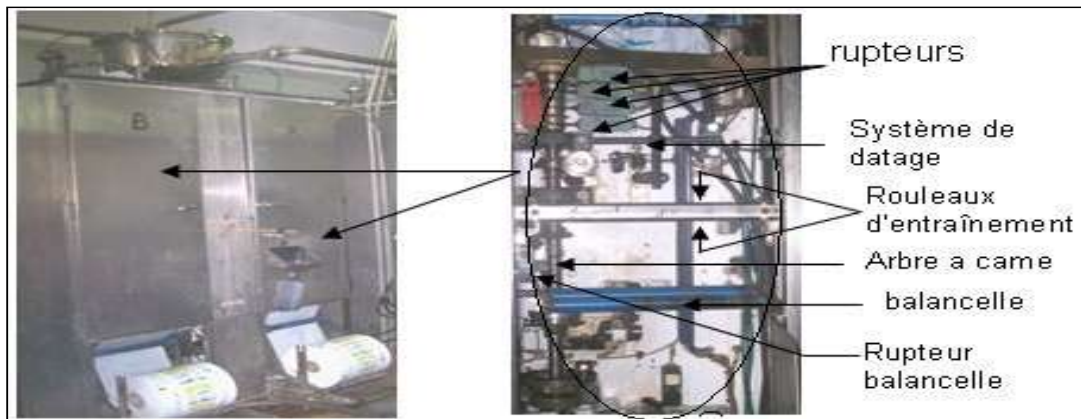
Emplacement de l'arbre à cames dans la machine.
